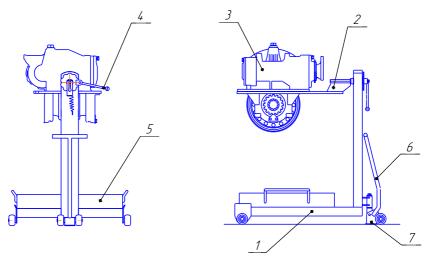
Эскиз стенда для ремонта редукторов: 1- основание; 2 — кронштейн; 3 — редуктор; 4 — рычаг фиксатора; 5 — ванна; 6 — ручка транспортная; 7 — пята.
